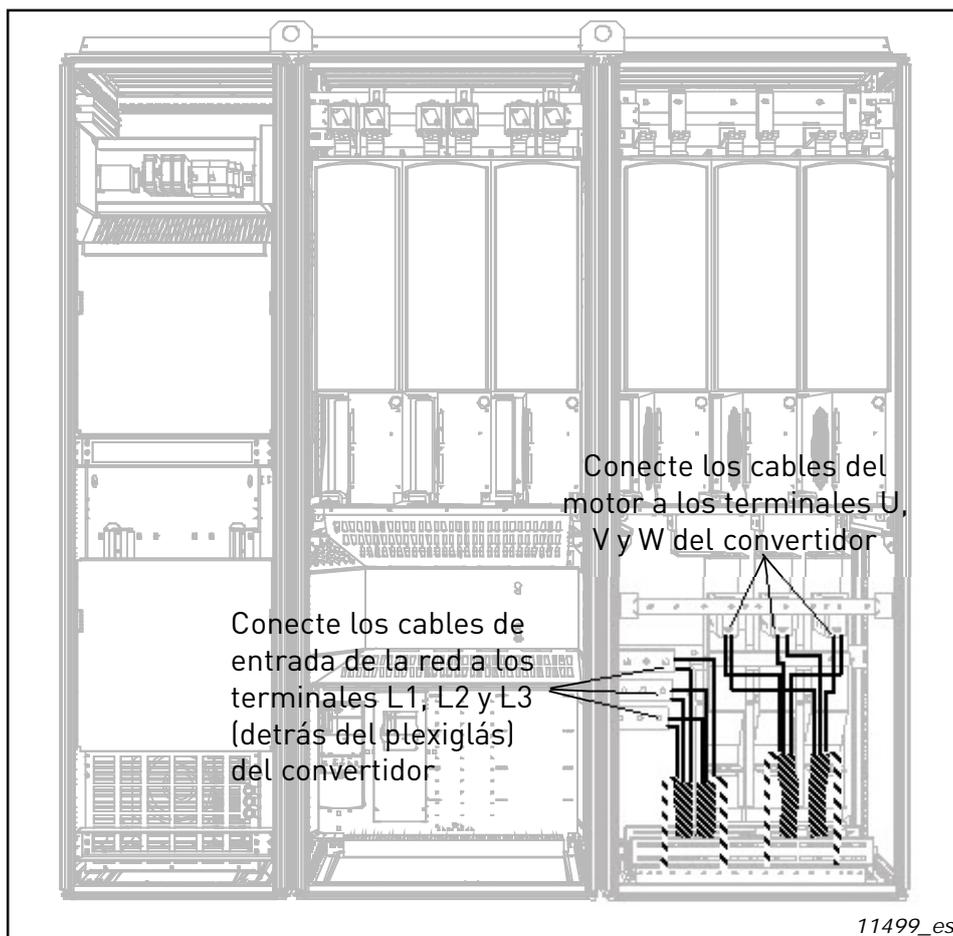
Colocación de los cables de alimentación, cableado inferior, bastidor AF13
